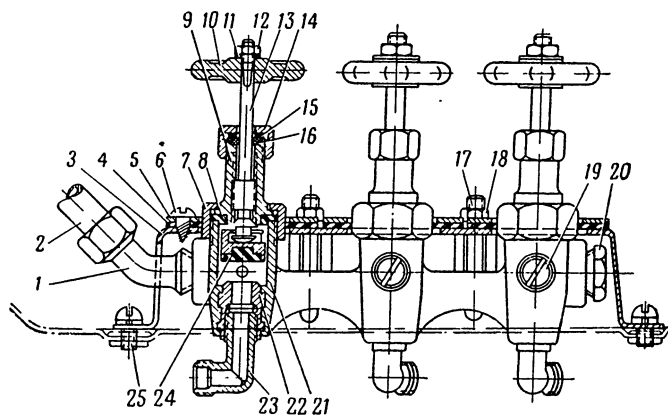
Конструктивная схема и схема крепления блока шинных кранов
